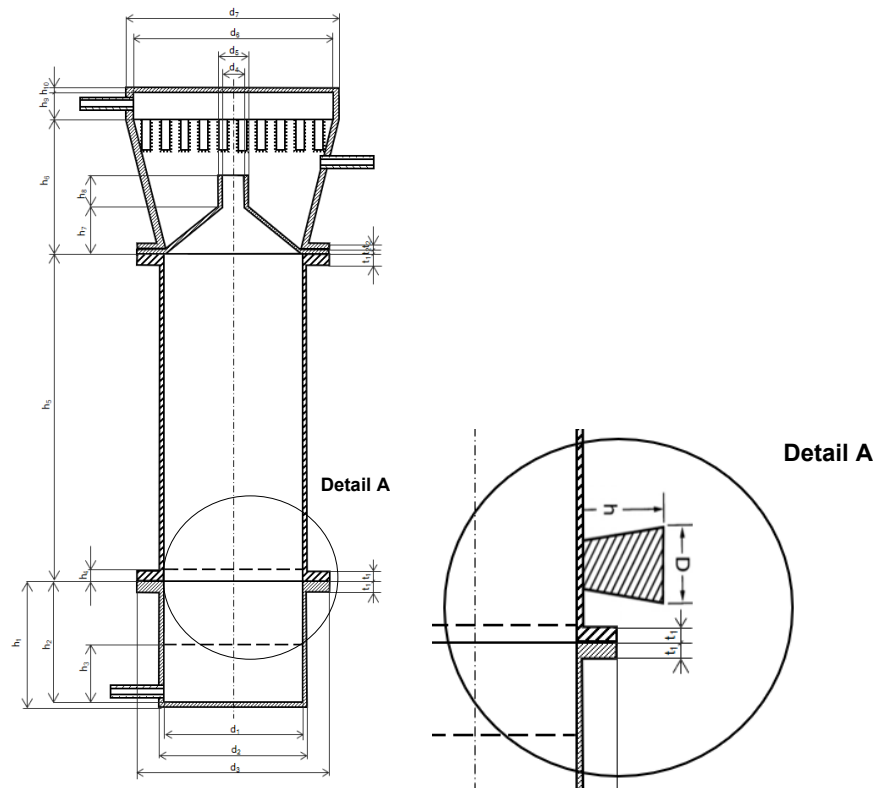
Prinzipskizze des Wirbelschichtreaktors mit Probenahmestelle - Detail A
